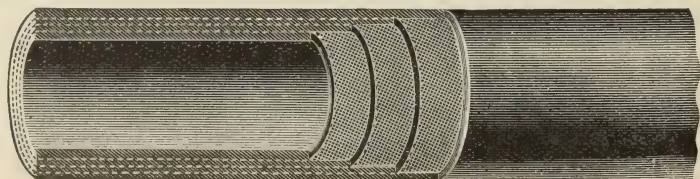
Leitungsschlauch mit Baumwolleinlagen
